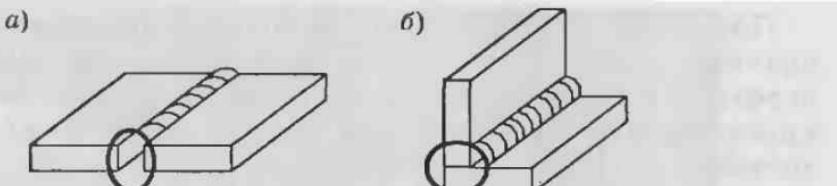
Типы сварных соединений: *а* — стыковое; *б* — угловое
